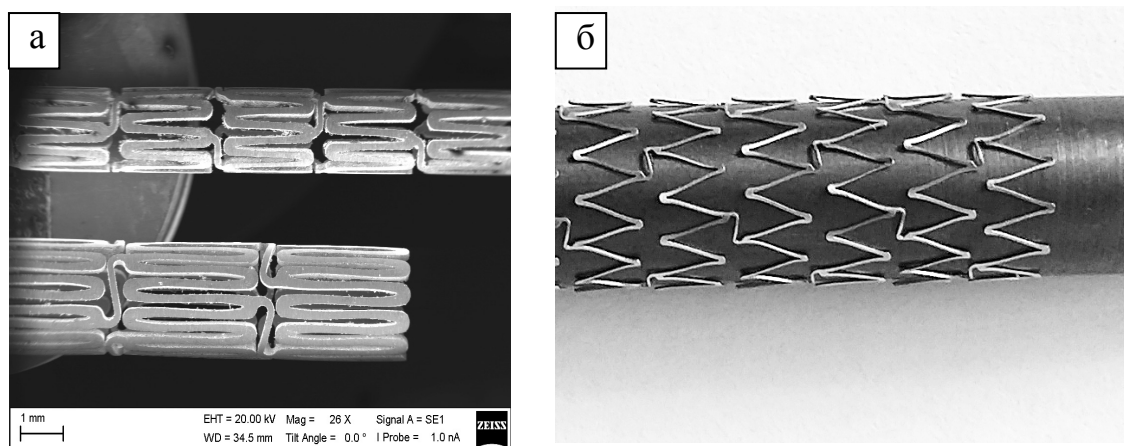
Заготовки стента двух типоразмеров после лазерной вырезки (а);
